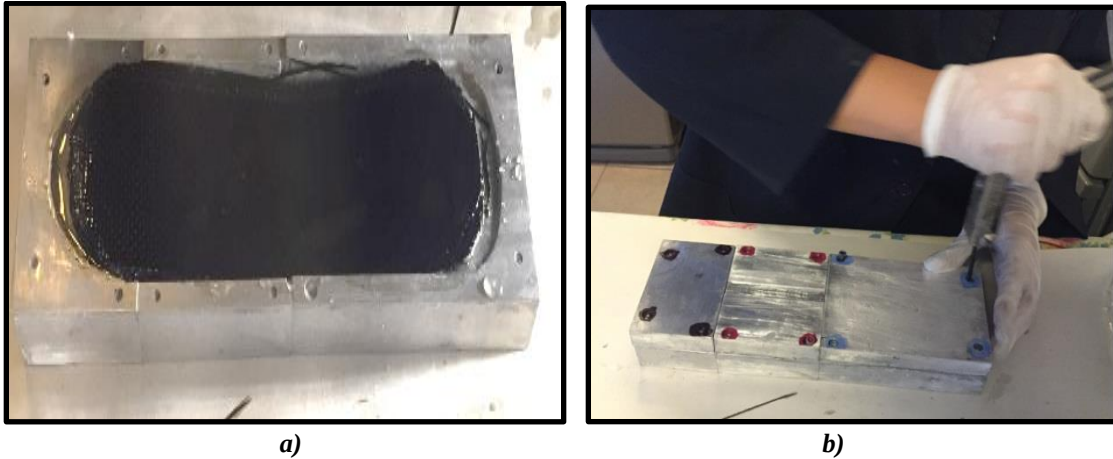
Manufactura de pieza inferior: a) Impregnación del laminado; b) Cerrado de molde.
